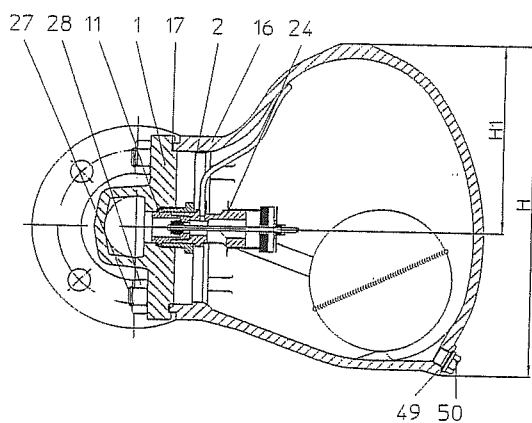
1 mit Flanschen - horizontale Einbaulage
